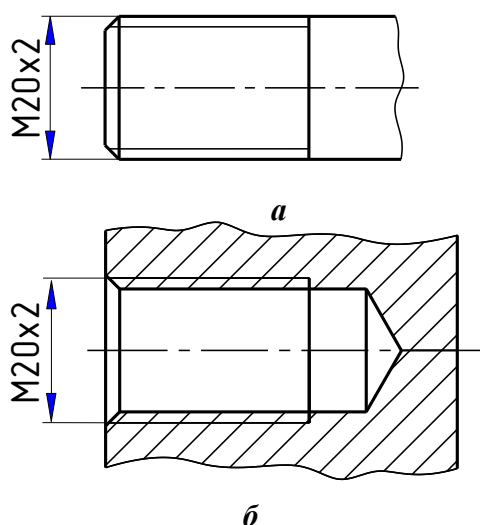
Обозначение метрической резьбы, нанесение ее размера:
